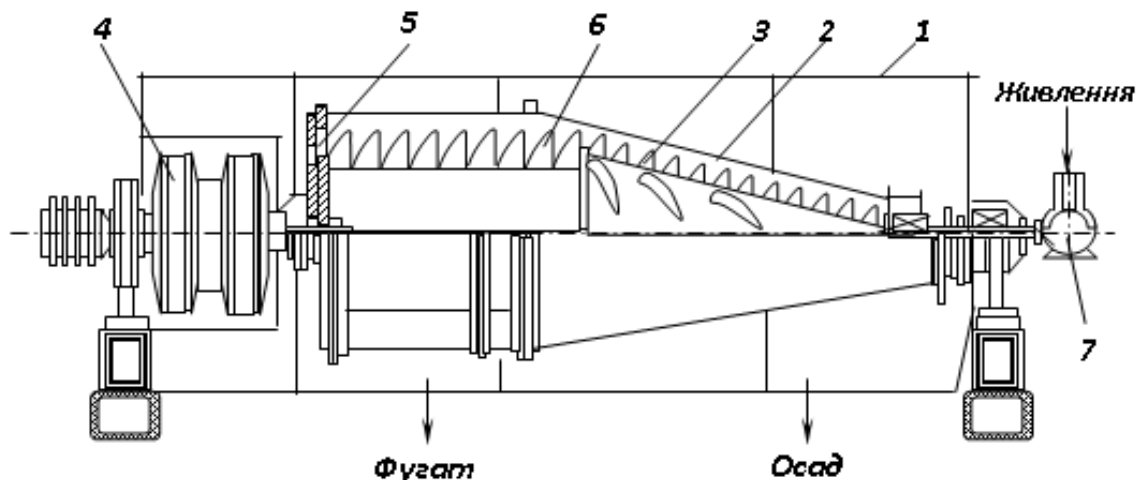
Осаджувальна шнекова центрифуга типу ОГШ: 1 – корпус, 2 – ротор, 3 – шнек, 4 – планетарний редуктор, 5 – зливні вікна, 6 – спіраль, 7 – завантажувальний пристрій.
